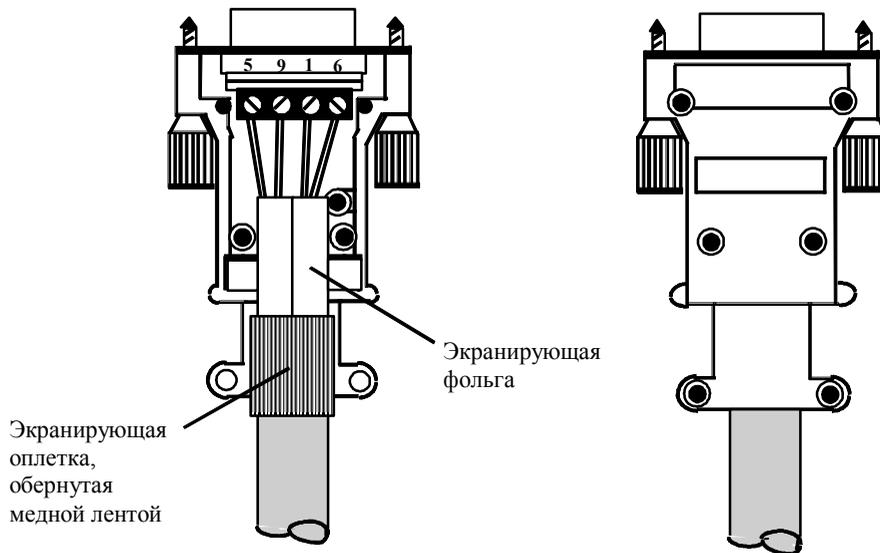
9-контактный sub-D штекер (вилка), смонтированный на стандартный кабель
